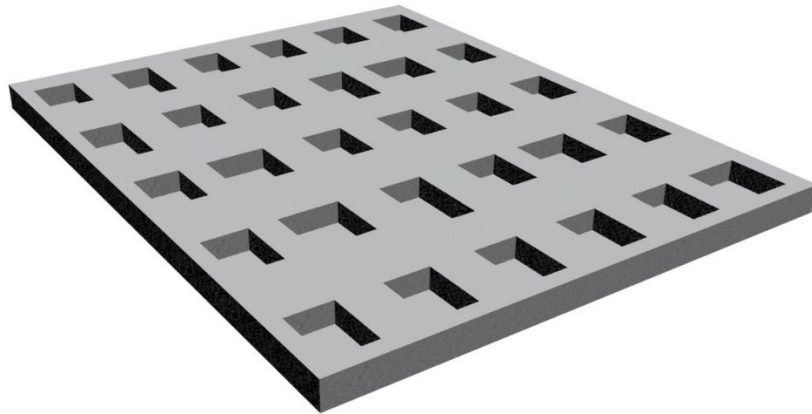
Detalle de cavidad para almacenaje de piezas
